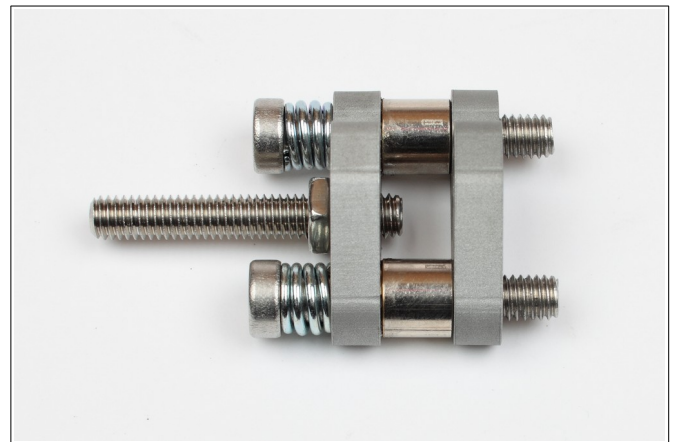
Anschließend wird die Magnetplatte angeschraubt, wobei die Schrauben nur soweit angezogen werden, bis die Federn blockieren.
